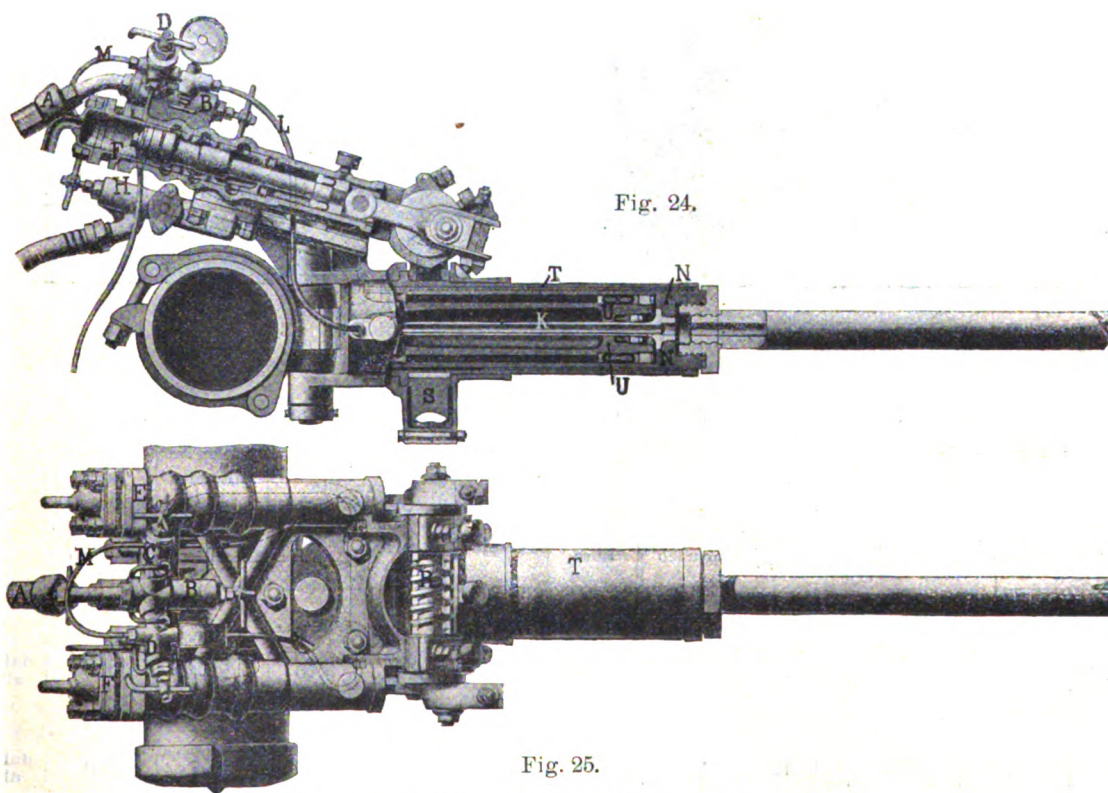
e 25. Sezione e pianta della perforatrice idraulica.
